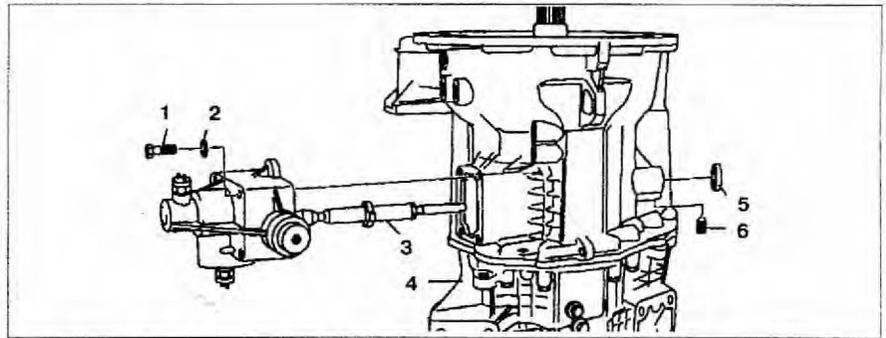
Снятие и установка механизма переключения передач: 1, 6 – Болты; 2 – Прокладка; 3 – Корпус механизма переключения передач; 4 – Коробка передач; 5 – Крышка.
